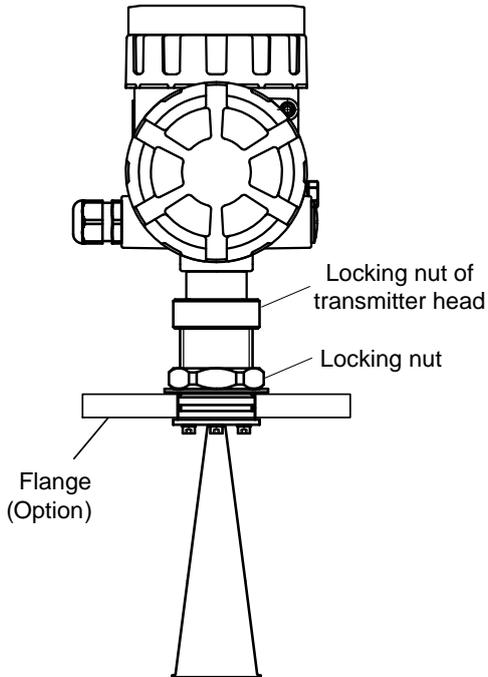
Fissaggio testa del trasmettitore
